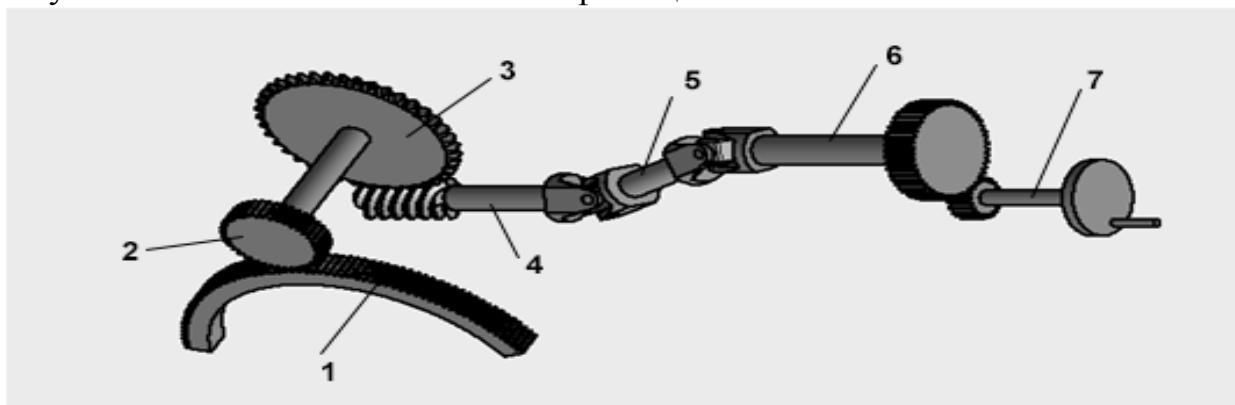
Загальний вигляд механізму: 1 – зубчатий сектор; 2 – шестерня; 3 – черв'ячне колесо; 4 – черв'як; 5 – шарнір; 6 – вал з шестернею; 7 – маховик;
